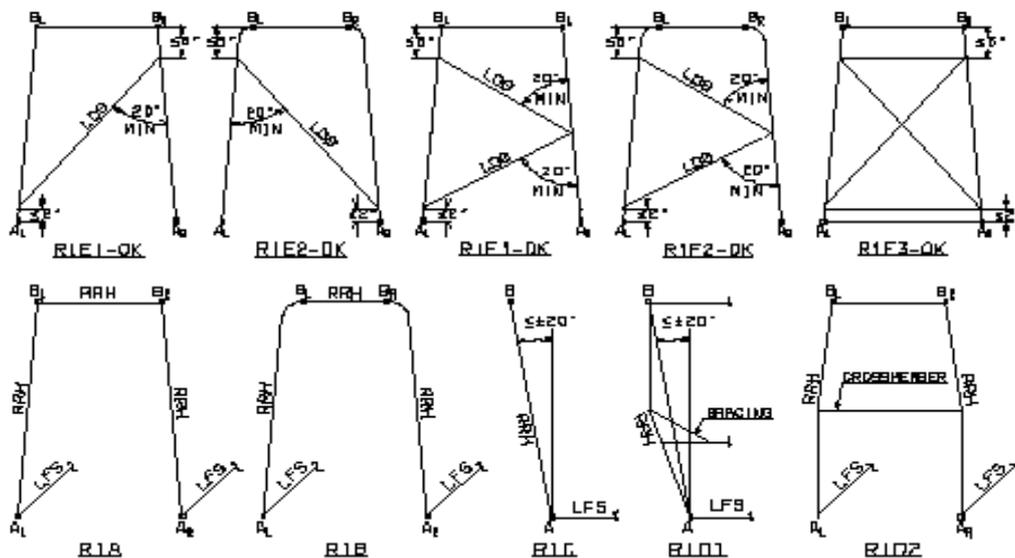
Configuración que debe de tener la parte posterior de la estructura y los refuerzos que puede llevar.
